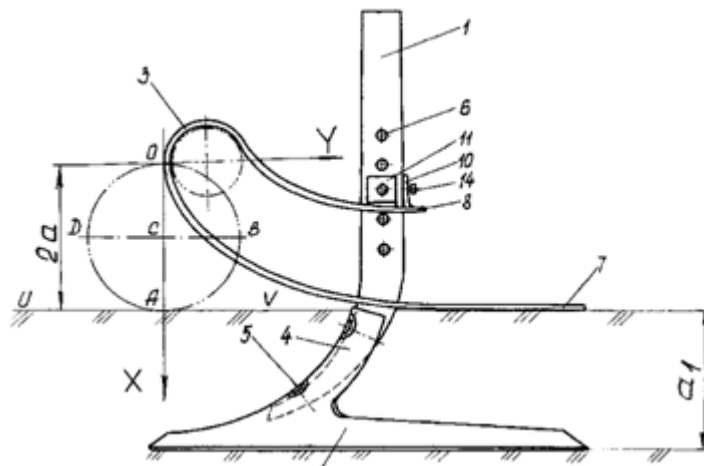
Робочий орган для обробки парів: 1 – стійка; 2 – універсальна стрілочаста лапа; 3 – деформатор; 7 – полоз; 8 – несуча площина.
